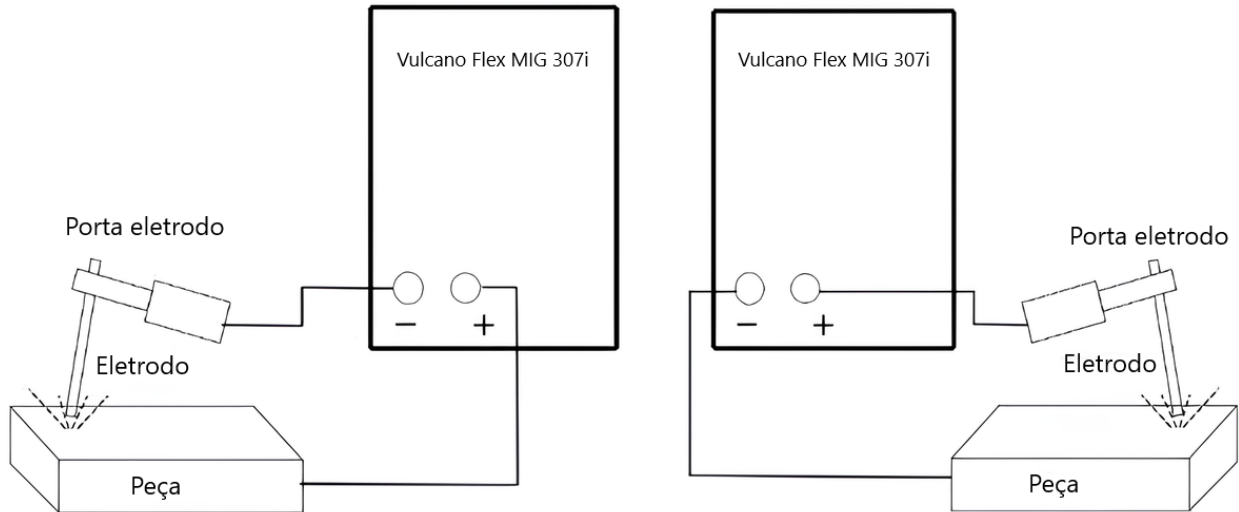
Conexão positiva e negativa para soldagem com eletrodo revestido.
